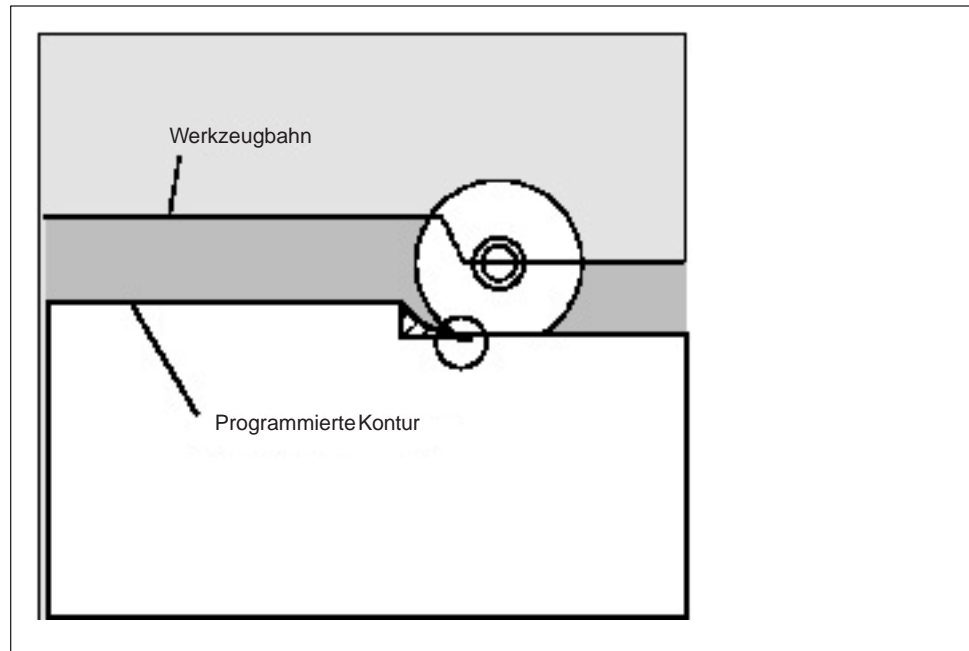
Der Konturweg ist kürzer als der Werkzeugradius.
